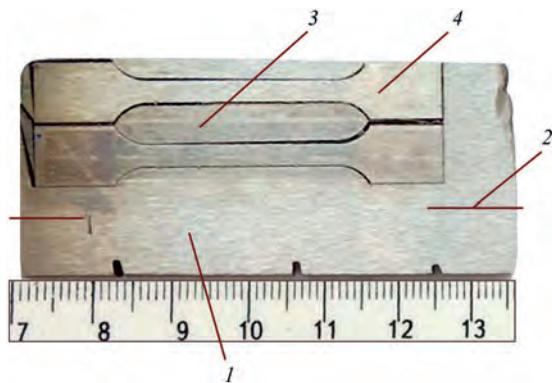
Схема виготовлення оптимізованого плоского пропорційного зразка наплавленого металу для високотемпературних випробувань наплавленого металу: 1 – технологічна основа з аустенітної нержавіючої сталі; 2 – положення лінії сплавлення з наплавленим металом; 3 – наплавлений метал жаростійкого або жароміцного сплаву; 4 – оптимізований плоский пропорційний зразок
